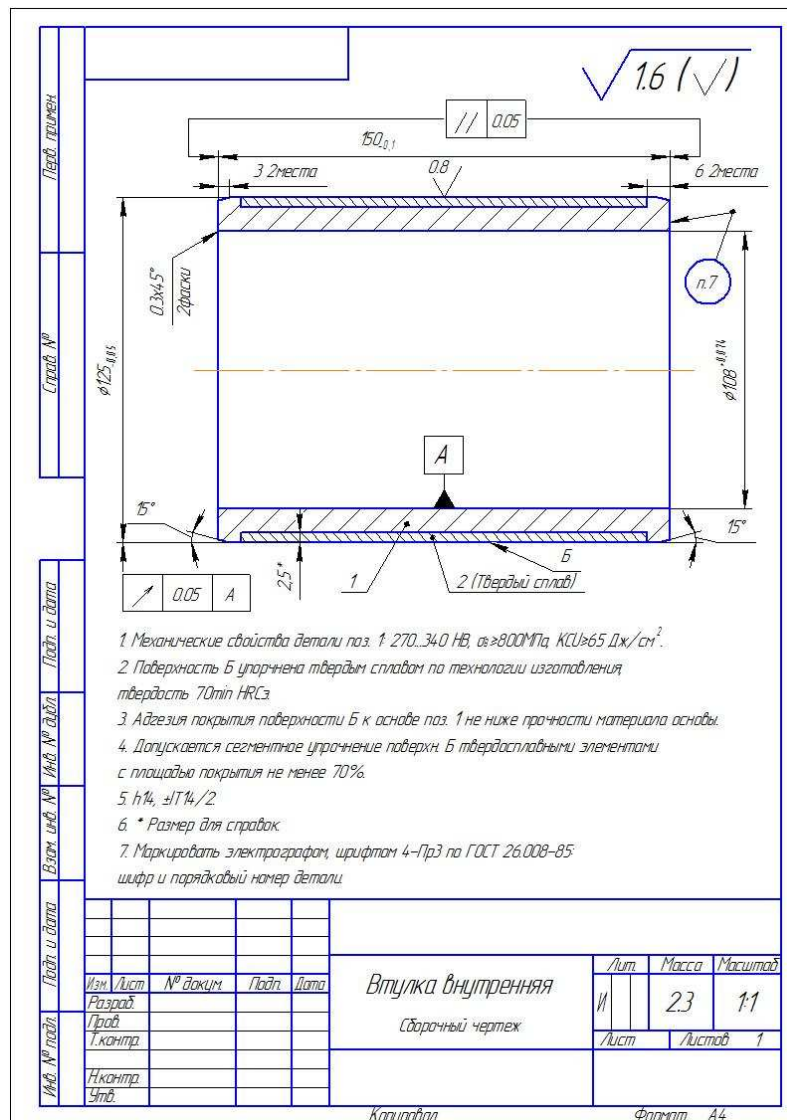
Сборочный чертеж детали «Втулка внутренняя»
